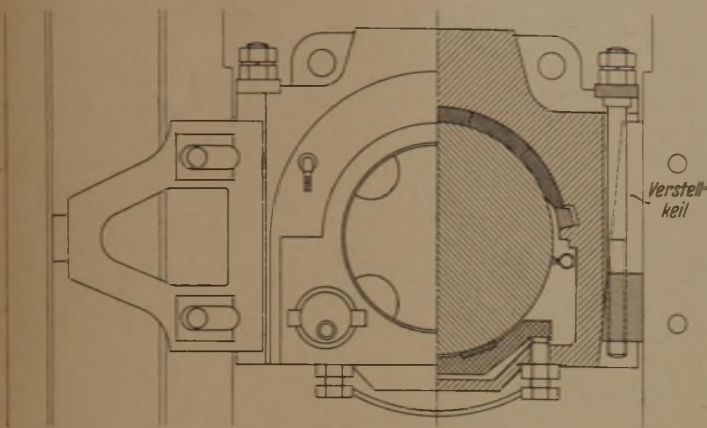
Einbaustück geschlossen, seitlich verstellbar.
